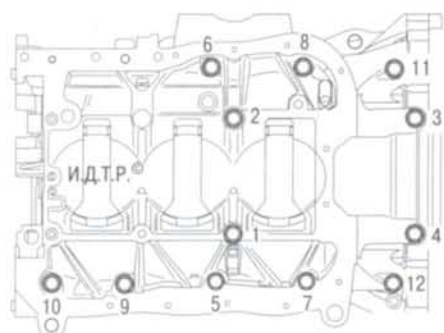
Порядок затяжки болтов крепления усилителя блока цилиндров
